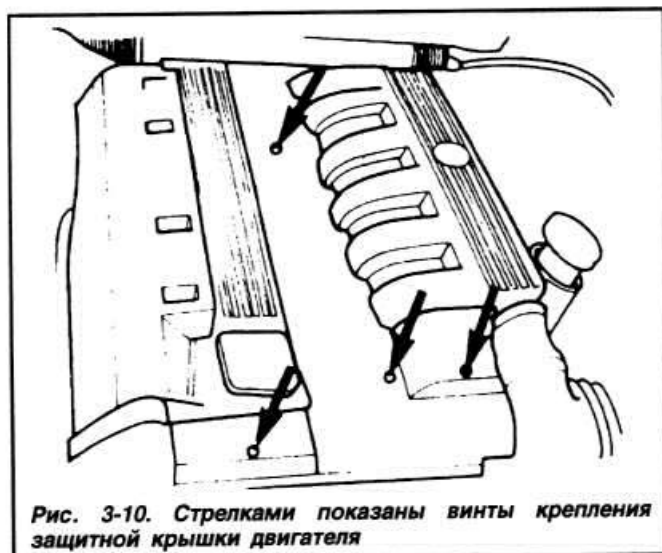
Стрелками показаны винты крепления защитной крышки двигателя
